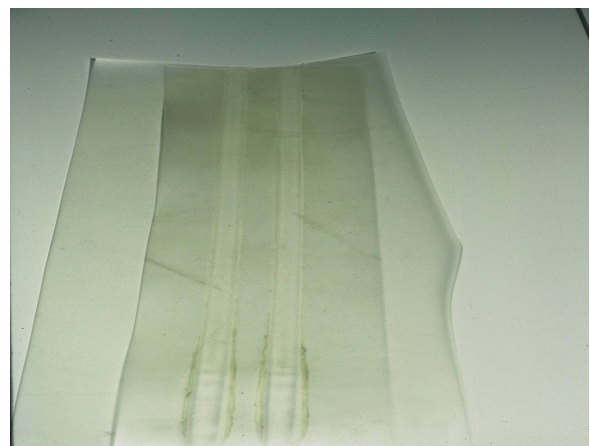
Géomembrane translucide soudée à la machine automatique - double soudure
